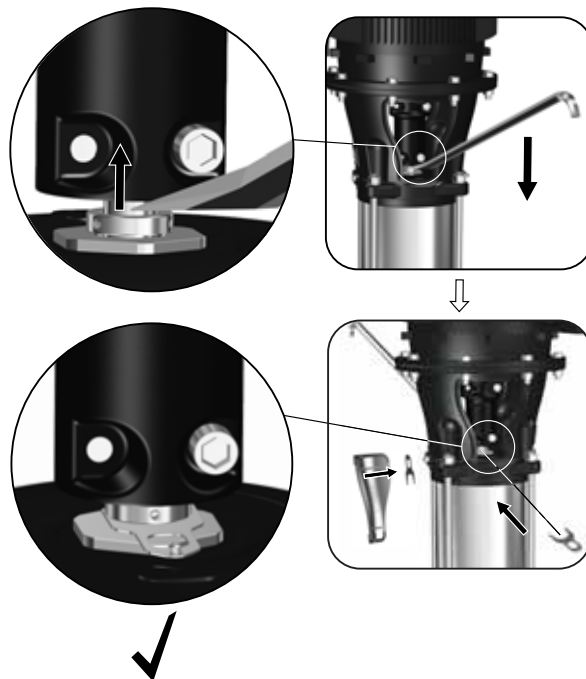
Подъем вала насоса и установка регулировочной вилки
